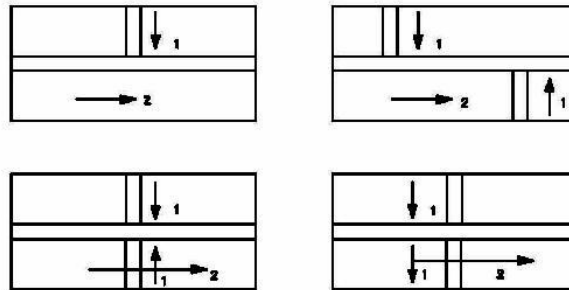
Placas unidas mediante soldadura, los números indican el proceso de soldadura.
